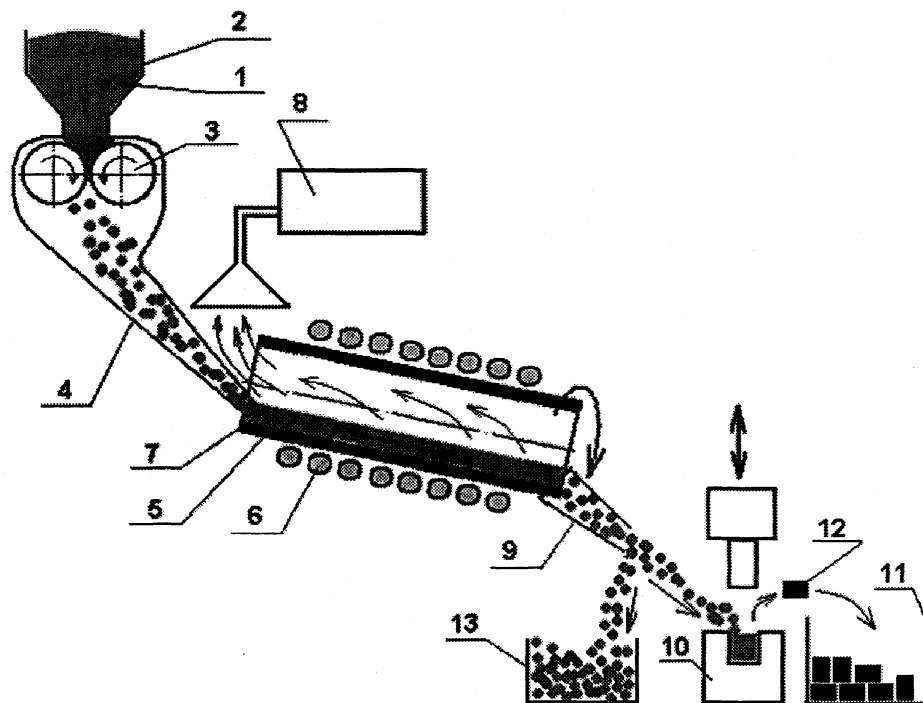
Способ подготовки и брикетирования стружки: 1 – стружка; 2 – бункер загрузки; 3 – дробилка; 4 – подающий лоток; 5 – барабан; 6 – индуктор; 7 – поток стружки; 8 – устройство нейтрализации; 9 – приемный лоток; 10 – брикетировочный пресс; 11 – тара для брикетов; 12 – брикет; 13 – тара для стружки
